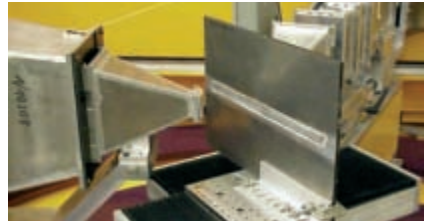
Bild GKSS: Zwei mit dem Reibrührschweißverfahren in Geesthacht zusammengefügte Aluminiumbleche. Zu sehen ist die Messung von Eigenspannung in der Schweißnaht mit Neutronen am Forschungsreaktor in Geesthacht.
